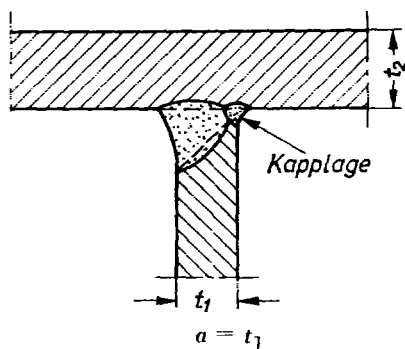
HV-Naht mit Kehlnaht (Kapplage gegengeschweißt)
